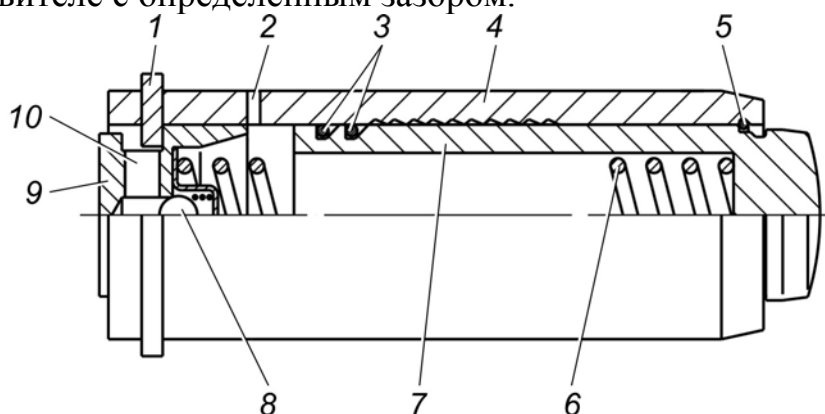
Б. Гидронатяжитель 406.1006100-50: 1 – кольцо; 2 – отверстие для перепуска масла; 3 – запорные кольца; 4 – корпус; 5 – стопорное кольцо; 6 – пружина; 7 – плунжер; 8 – шариковый клапан; 9 – дроссель с клапаном в сборе; 10 – отверстие для подвода масла
